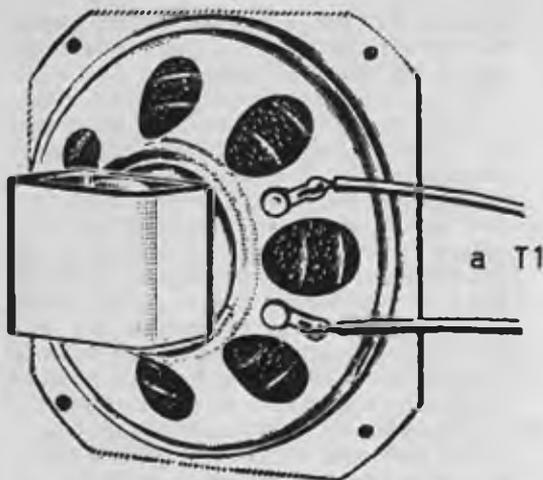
L'altoparlante deve essere inserito sul quattro perni di plastica sporgenti nella parte interna del pannello frontale; fondendone la parte iniziale, con il saldatore, si determinerà il fissaggio definitivo dell'altoparlante al mobile; i due terminali della bobina mobile, che vanno collegati al trasformatore d'uscita, dovranno rimanere rivolti verso l'alto.
